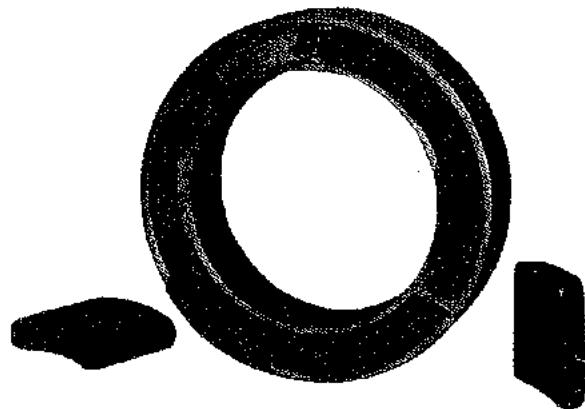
Muela de segmentos (Blanchard Machine Co.)
